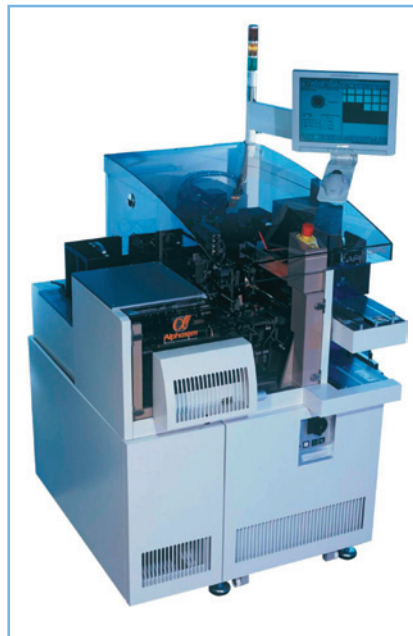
Eine Die-Attach-Maschine wie die »Easyline 8032« montiert Chips in ihre Gehäuse
